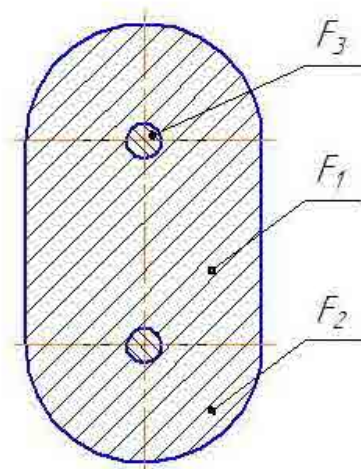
До розрахунку площі поверхні заготовки
